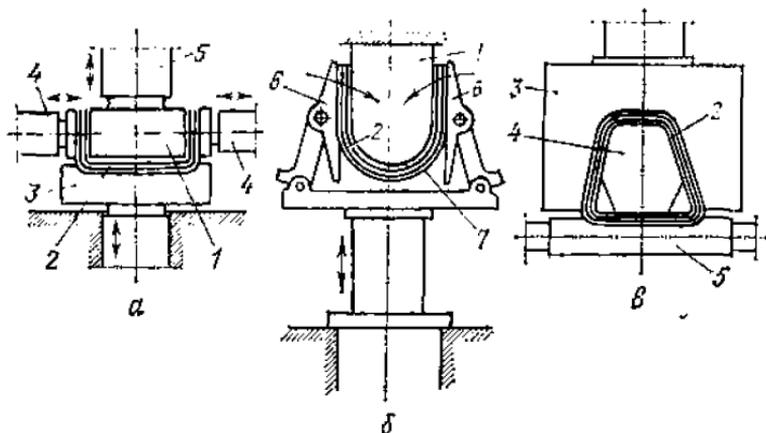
Схема устройств для склеивания криволинейных заготовок из шпона:
